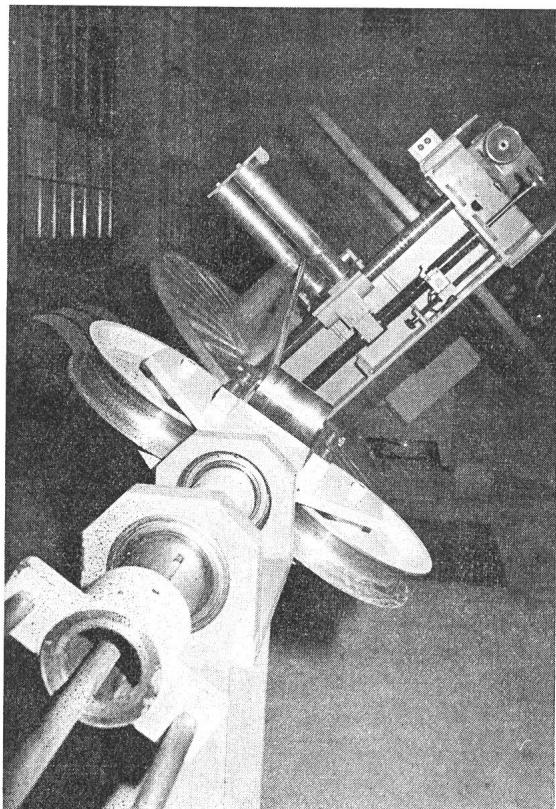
Rotationsanlage für Kabel mit grösserem Querschnitt
